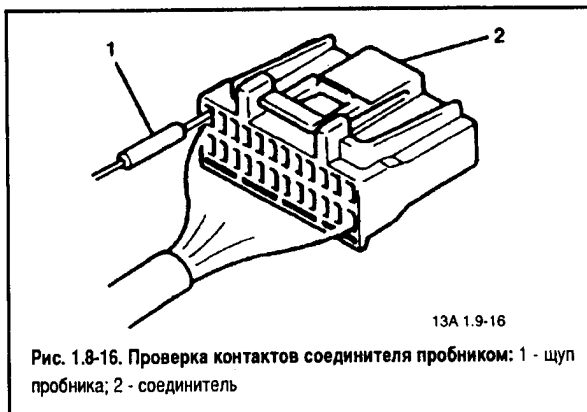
Проверка контактов соединителя пробником: 1 - щуп пробника; 2 - соединитель
